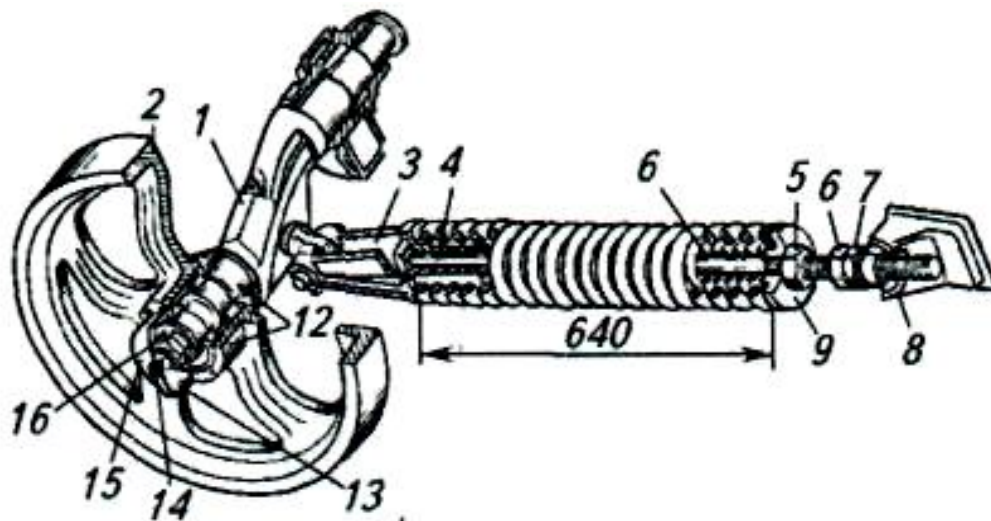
Натяжное устройство трактора с балансирной подвеской
